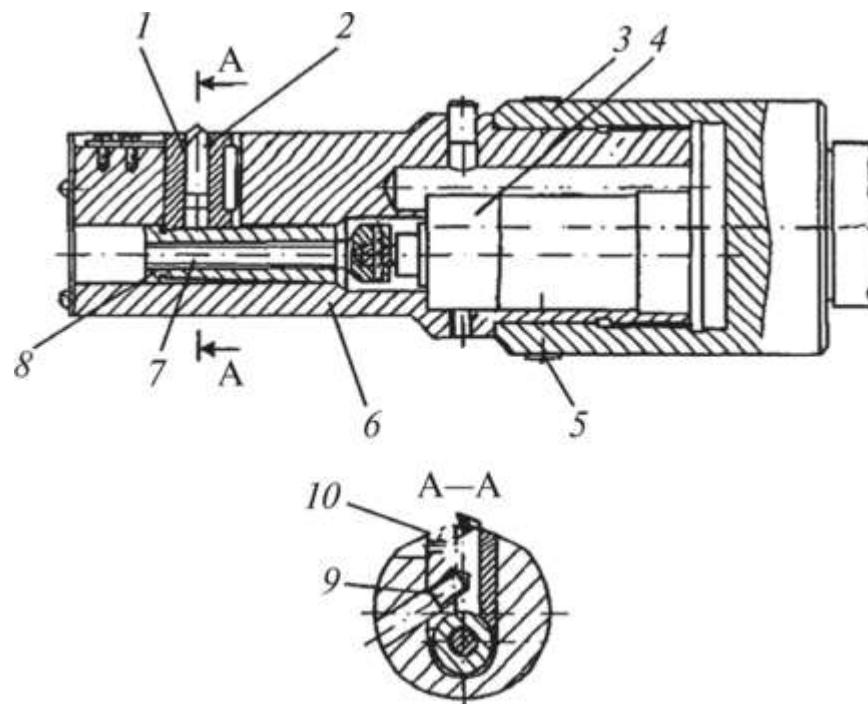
Схема автоматичного регулювання гвинта різальної кромки різця в розточувальній оправці
